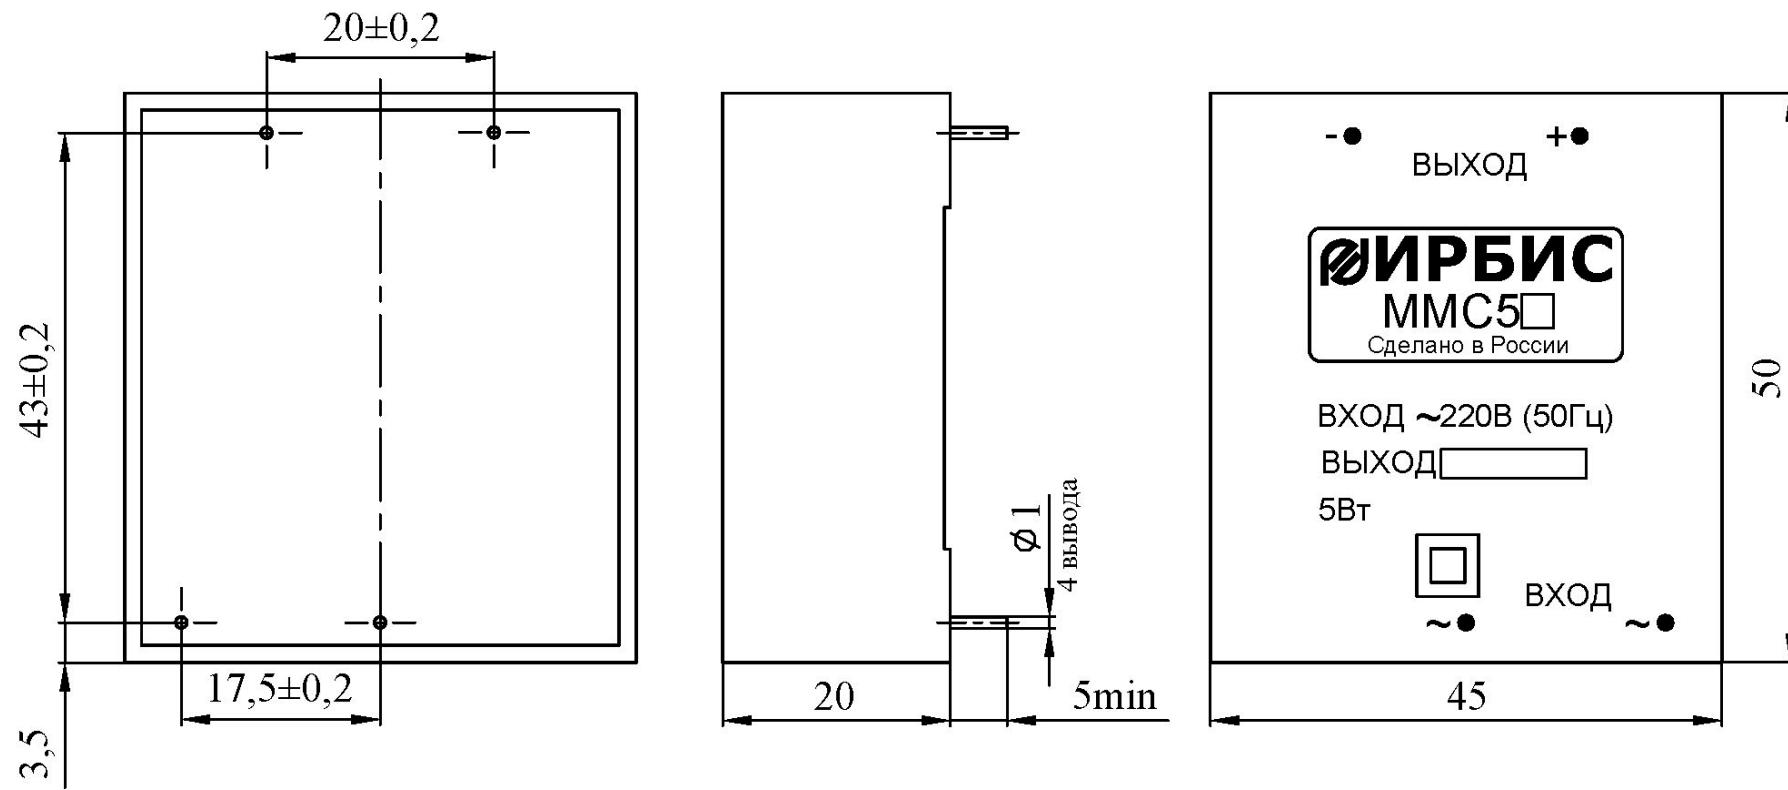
Габаритный чертеж модулей серии MMC5
